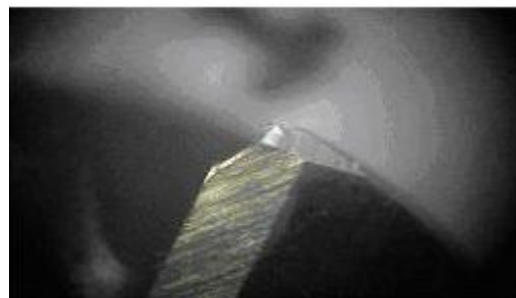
Внешний вид боковой поверхности и следы ударов фрезы по поверхности образца №7
